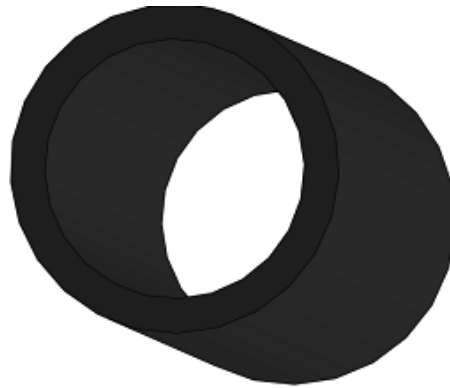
Dispositivo interno después de ser mecanizado vista frontal y superior.
